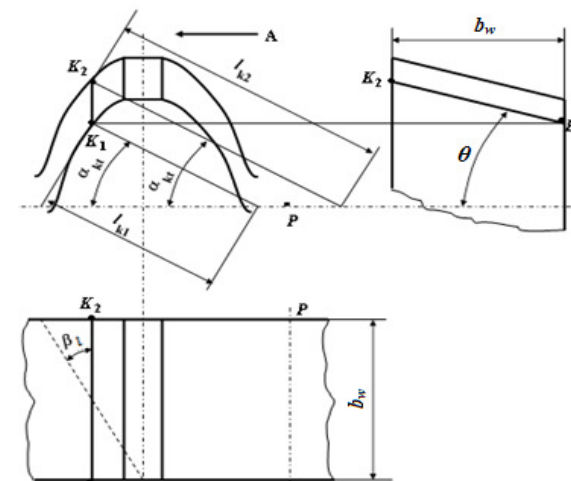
Головка зуба исходной рейки цилиндрической передачи Новикова со спрямленными зубьями в трех проекциях
